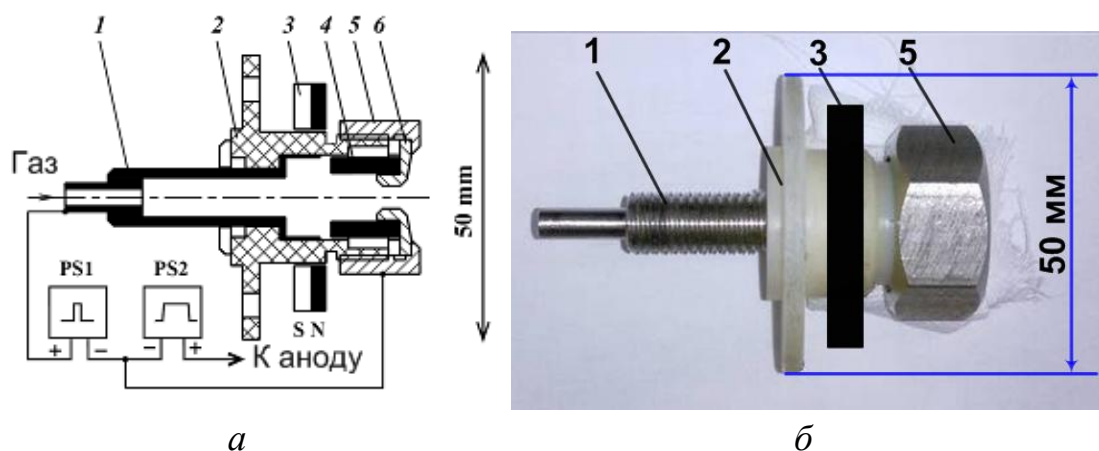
Конструкция катодного узла (а) и его внешний вид (б):
